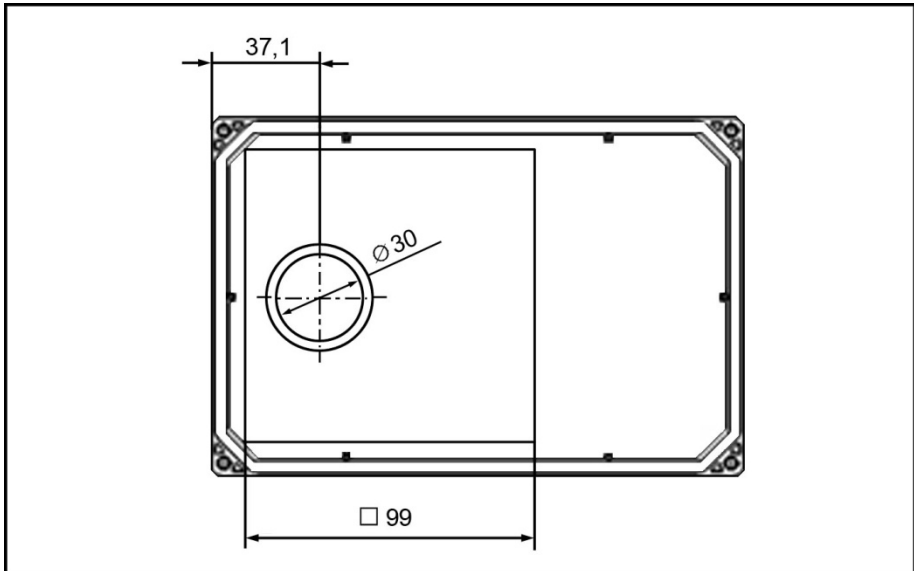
Bohrbild Standard-Adapterplatte BG α
